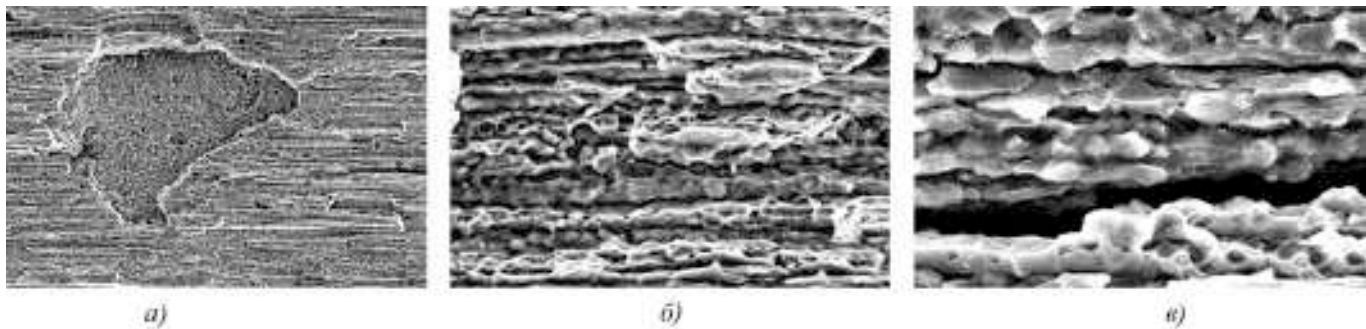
Строение излома сварного соединения прессованной полосы толщиной 40 мм, корень шва:
